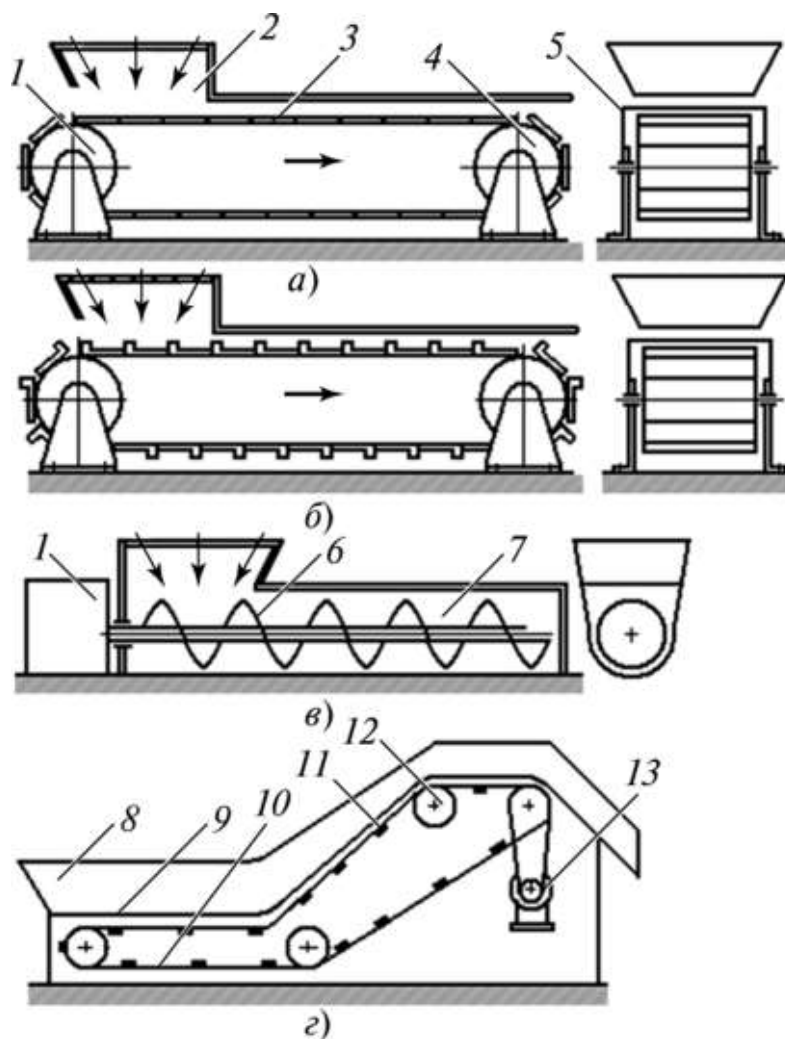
Принципові схеми конвеєрів для видалення і транспортування стружки від робочих зон верстатів:
